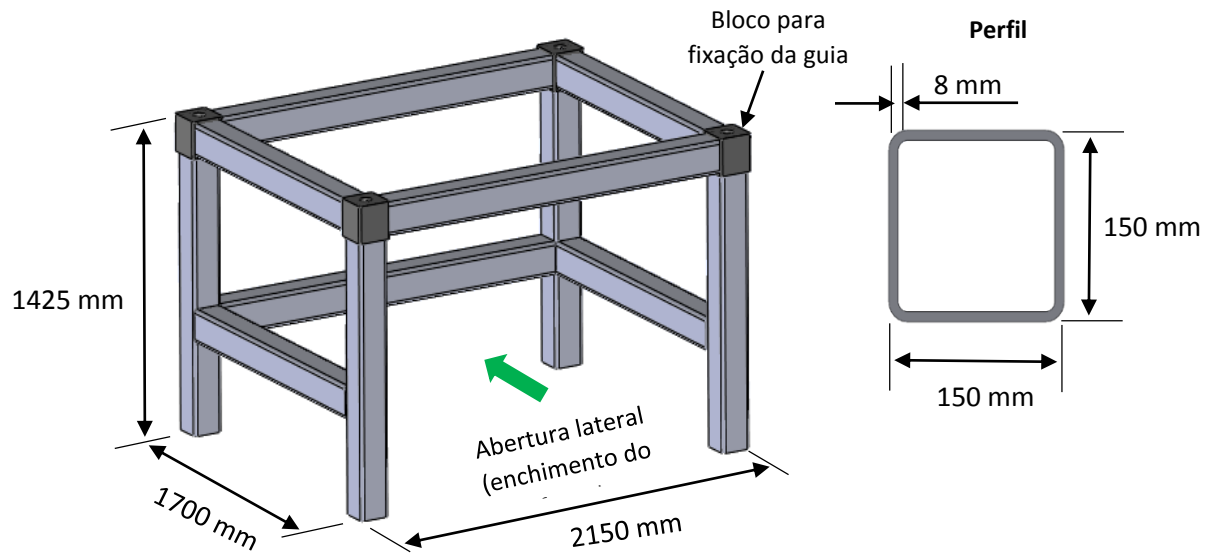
Modelação 3D da base de suporte em estrutura soldada: perfil de secção quadrado (150x150x8 mm).
